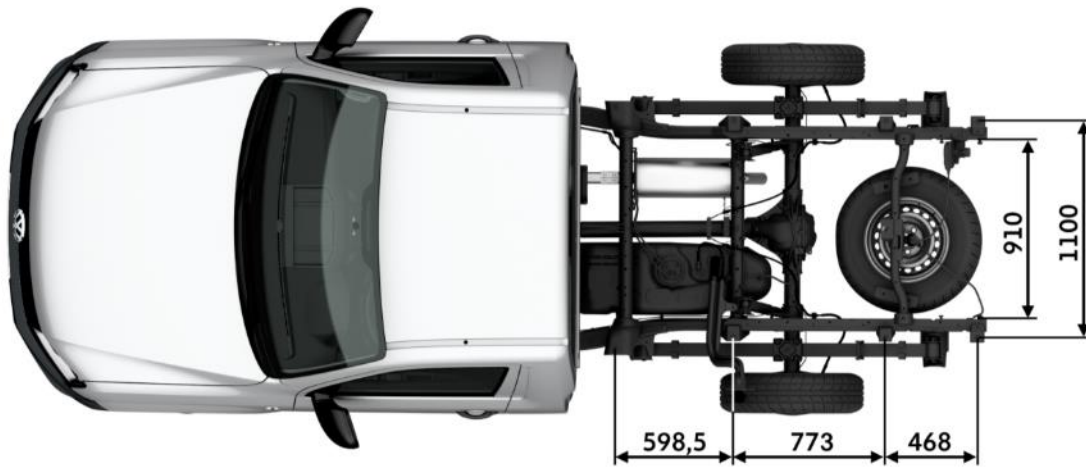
Draufsicht Amarok-SC (Single Cab) ohne Cargobox
